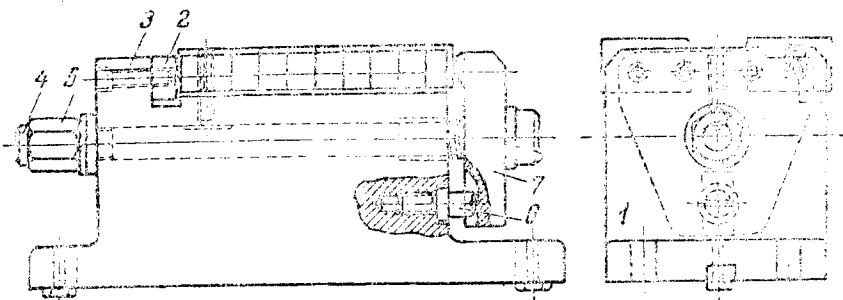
Момент фрезерования (III, IV и V операций) кулачка
